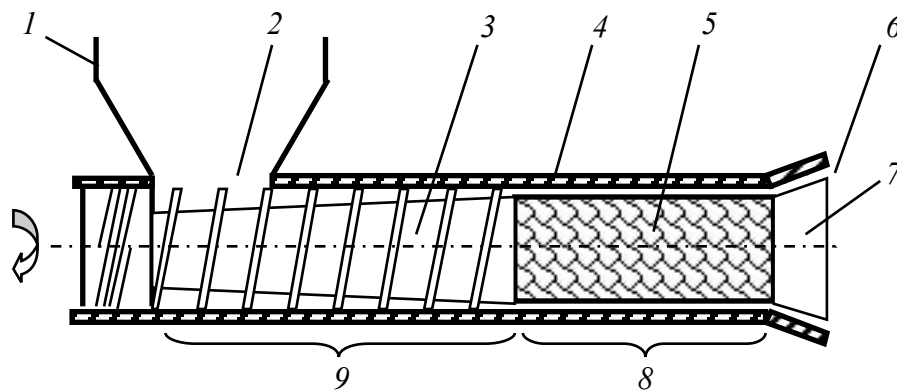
Принципова схема обладнання роторного подрібнювача:
